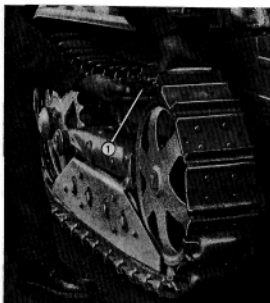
Impiego della maniglia (1) per montaggio e smontaggio soprapattini.
